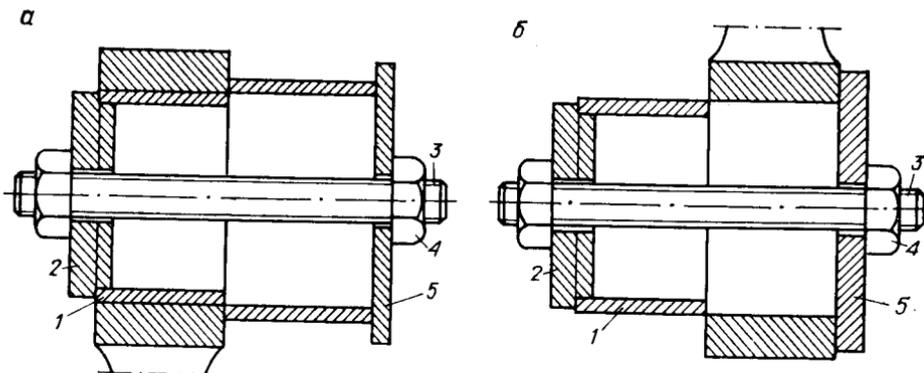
Приспособление для выпрессовки (а) и запрессовки (б) втулок крейцкопфной головки шатуна:
